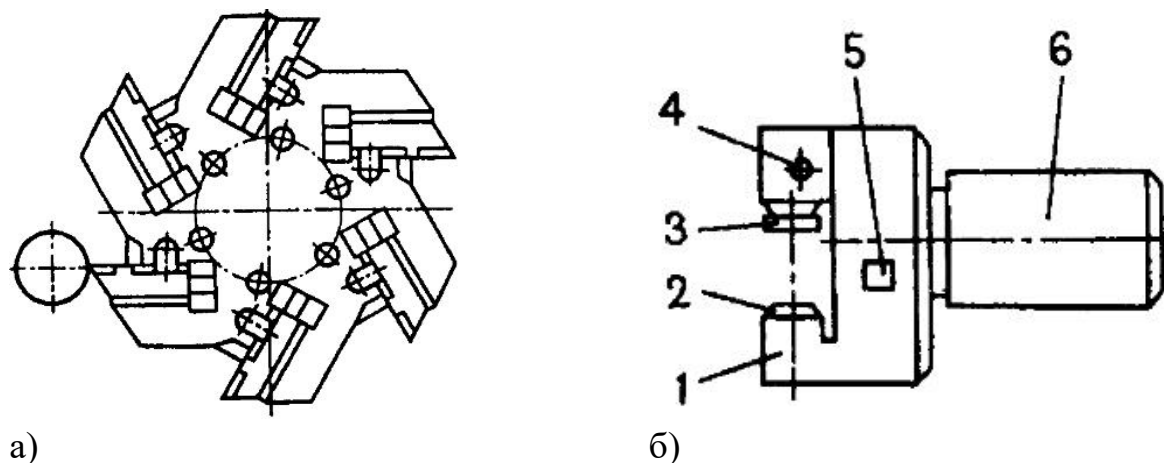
Інструментальна головка токарного верстату з ЧПК (а) та інструментальний різцевий блок
